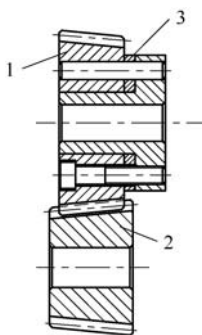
圆柱齿轮轴向垫片间隙消除机构
